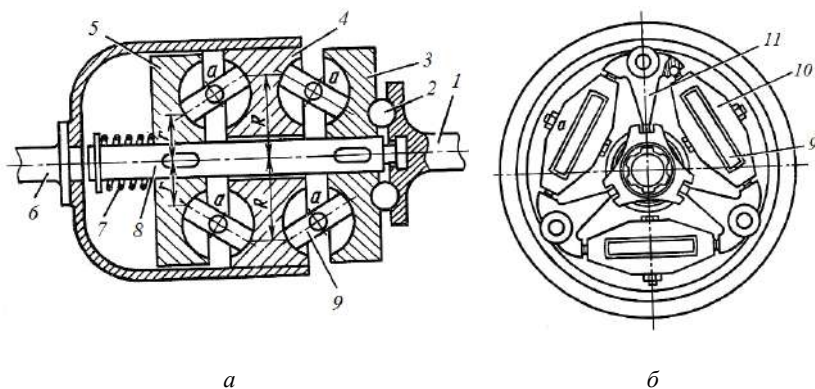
Фрикційний тороїдальний варіатор: 1 – ведучий вал; 2 – навантажувальний пристрій; 3, 5 – ведучі диски; 4 – ведений диск; 6 – ведений вал; 7 – пружина; 8 – вал; 9 – ролики; 10 – обойма; 11 – важелі
